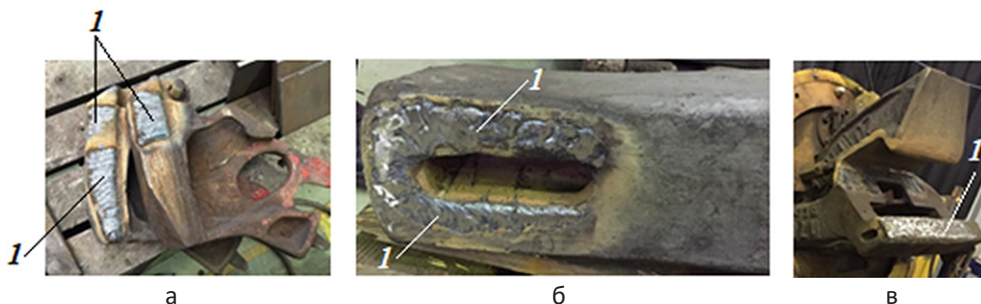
Поверхности корпуса автосцепки, регулярно подвергающиеся износу и поломке
